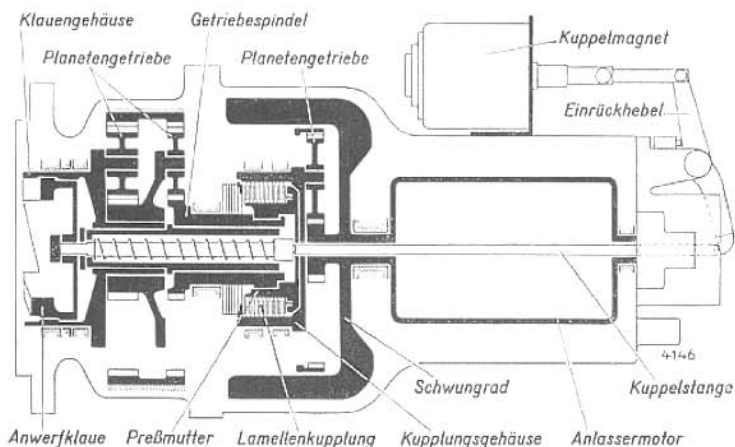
Räderschema des Bosch-Schwungrad-Anlassers
